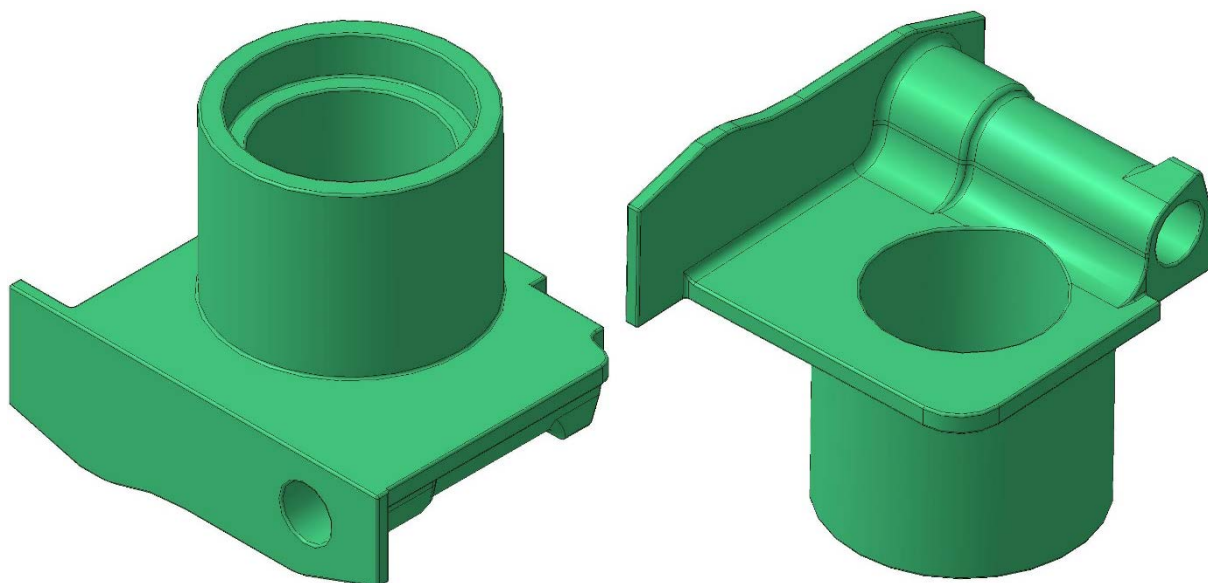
3D-модель заготовки детали «Корпус червячного редуктора»
